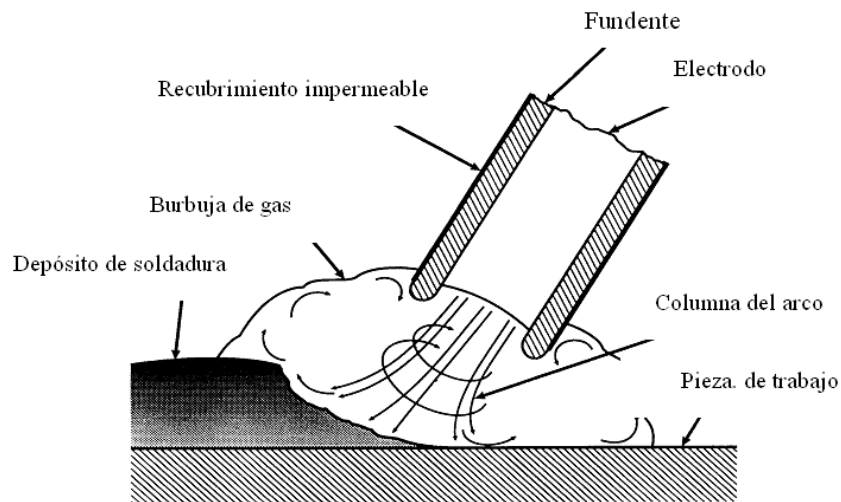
Arco eléctrico de soldadura submarina [11].
